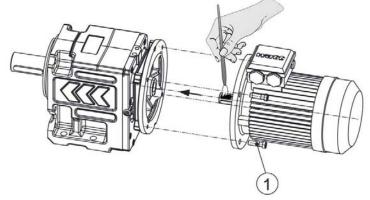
Prinzipdarstellung Montage Normmotor an IEC-Adapter
